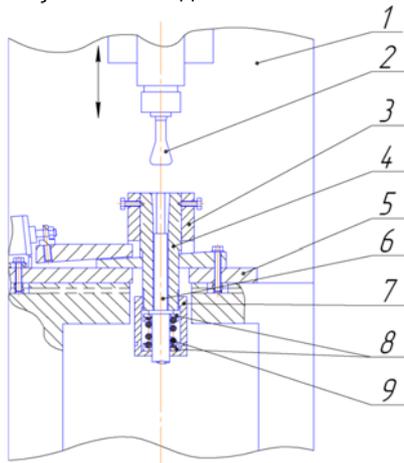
Установка для формирования конуса Морзе на электродах контактной сварки
